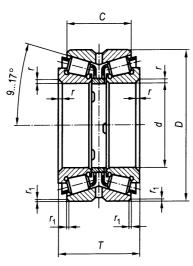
Подшипник роликовый радиально-упорный конический двухрядный
